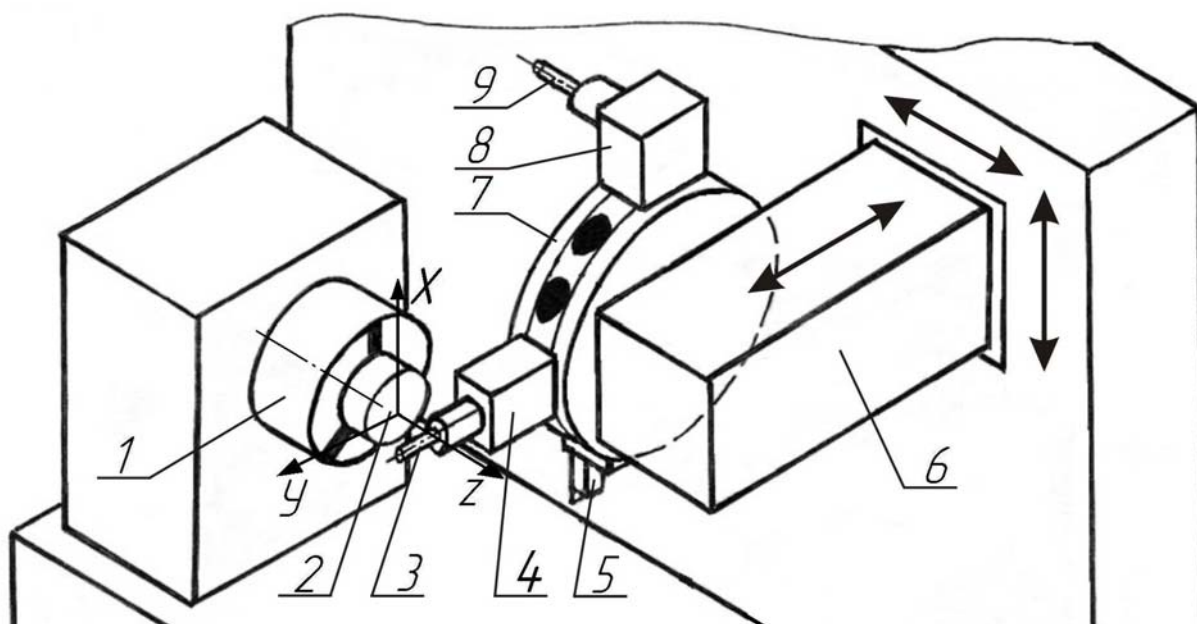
Структурная схема токарно-фрезерного многофункционального центра: 1 – шпиндель; 2 – деталь; 3, 9 – фрезы; 4 – фрезерный блок обработки детали в плане $Y-Z$; 5 – токарный резец; 6 – элемент крепления револьверной головки; 7 – револьверная головка; 8 – фрезерный блок обработки детали в плане $X-Y$
